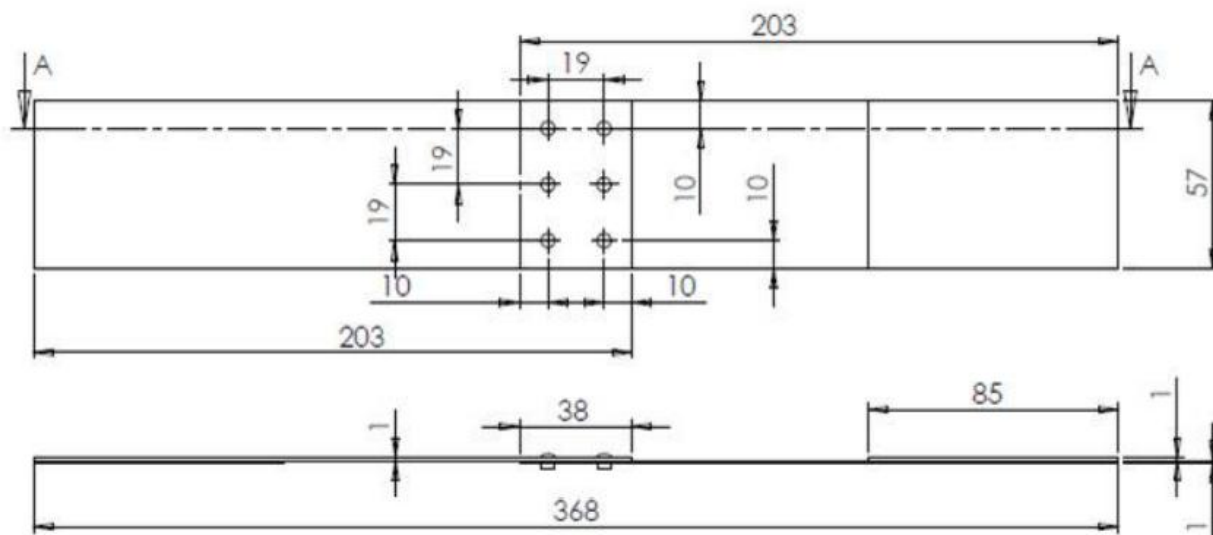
Зразок типового заклепкового з'єднання в конструкції легкого літака [58].
